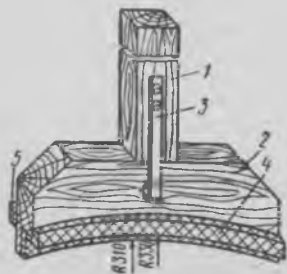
Приспособление для обработки концов ламелей коллекторов тягового двигателя НБ-412^М:
